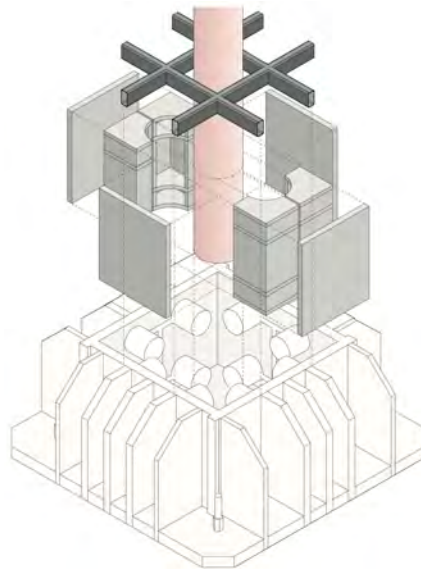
Ilustração esquemática da montagem do dispositivo de ensaios
